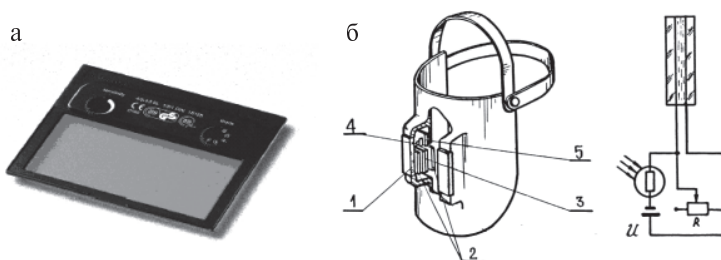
а — светозащитный блок [92]; б — схема светозащитного шлема для сварки: 1 — защитное стекло; 2 — поляроидные пленки; 3 — ЖКЭ; 4 — фоторезистор; 5 — источник питания
